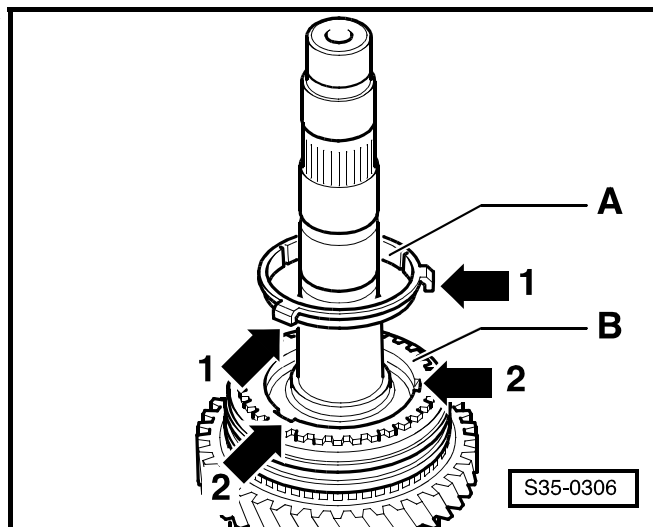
Положение для сборки шестерни 1-ой и 3-ей передач
